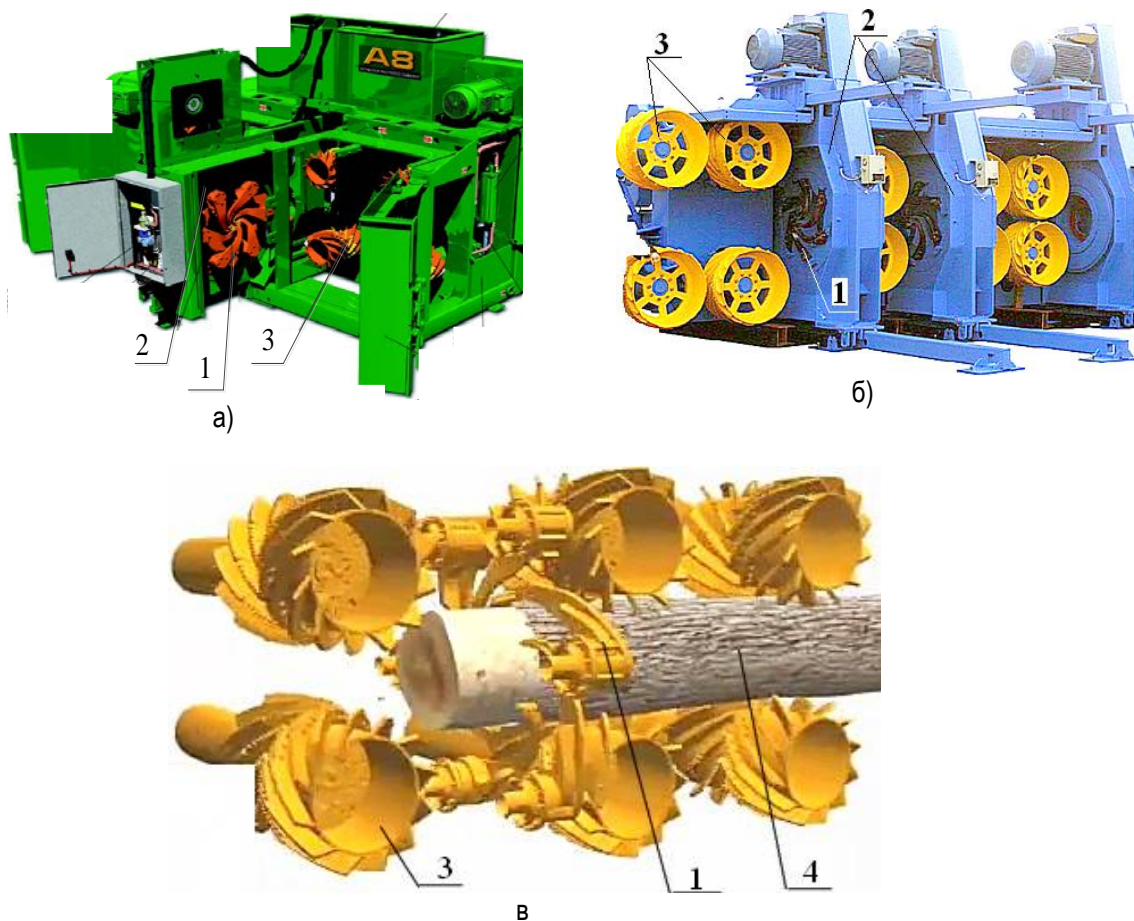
Окорка лесоматериалов на роторном окорочном станке: а – общий вид станка окорочного станка марки «Nicholson A8»; б – общий вид окорочного станка марки «VK»; в – схема обработки лесоматериала; 1 – коросниматель; 2 – ротор; 3 – вальцы подачи; 4 – лесоматериал
